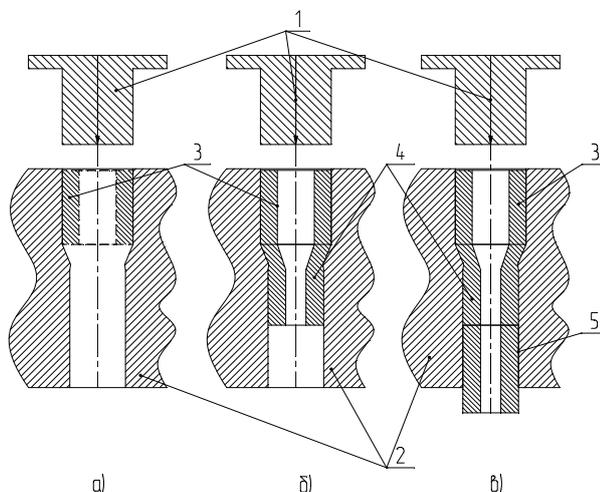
1-пуансон; 2-матрица; 3, 4,-деформируемые заготовки, 5-готовая поковка (деталь)
